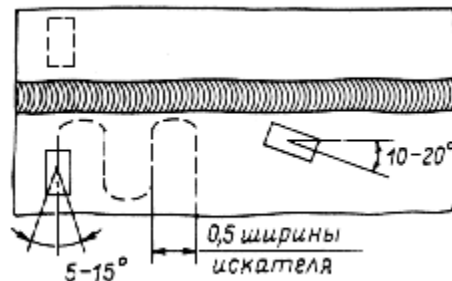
Схема перемещения искателя при контроле сварного соединения
